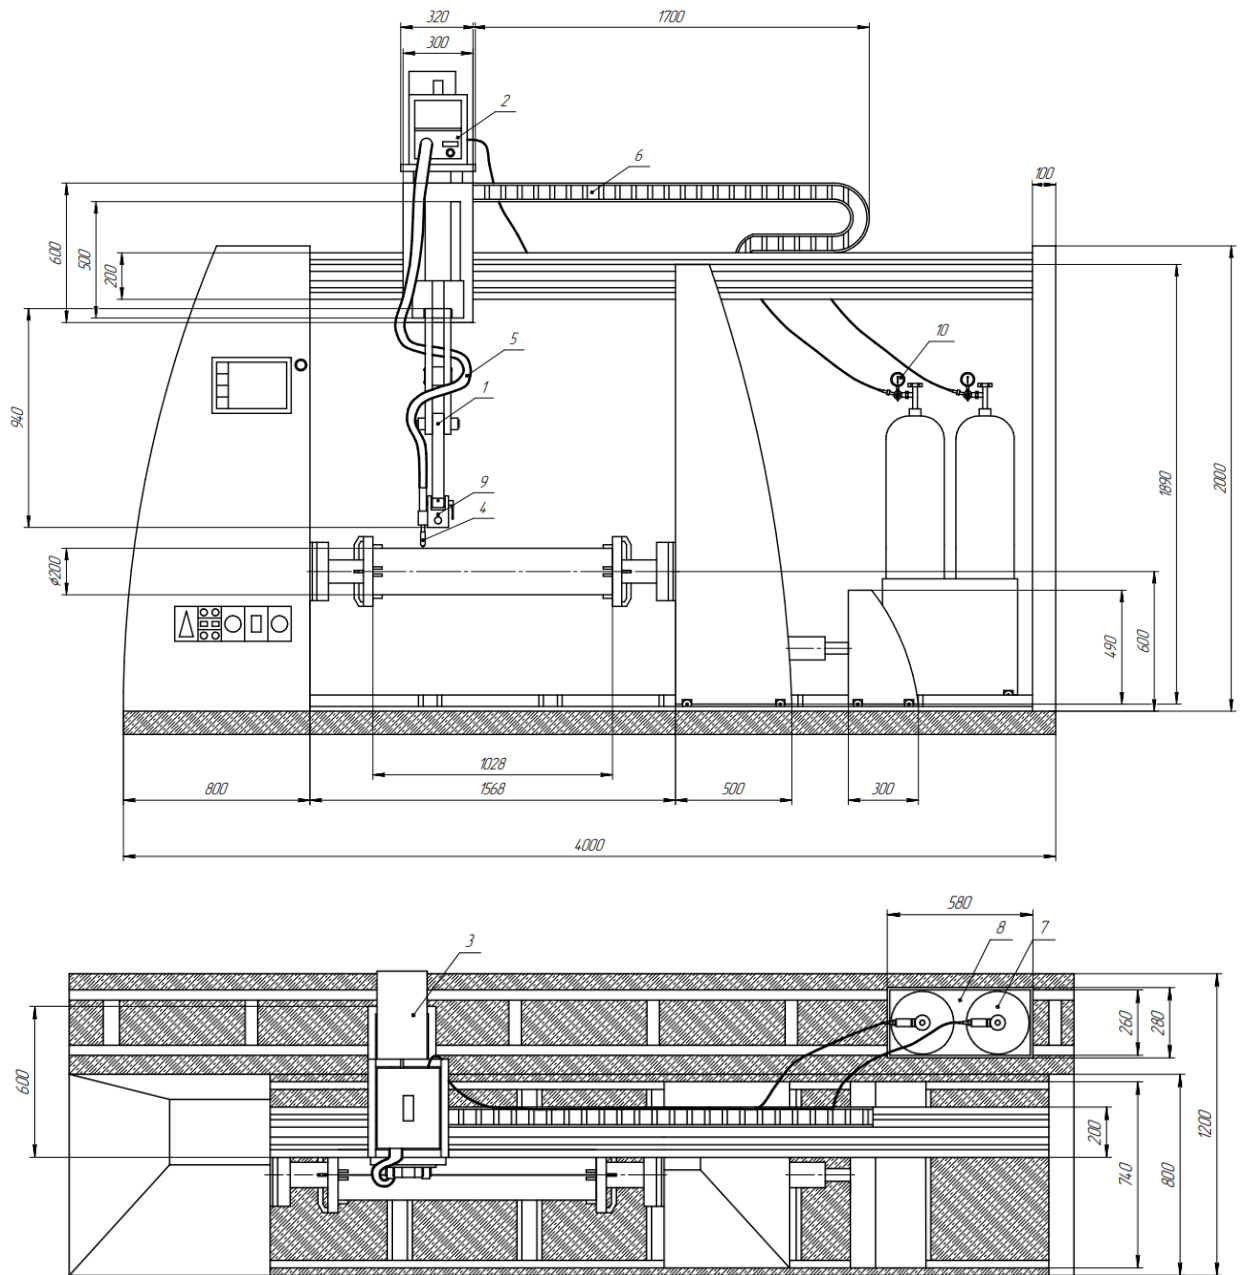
Установка для зварювання швів № 1,2,3
